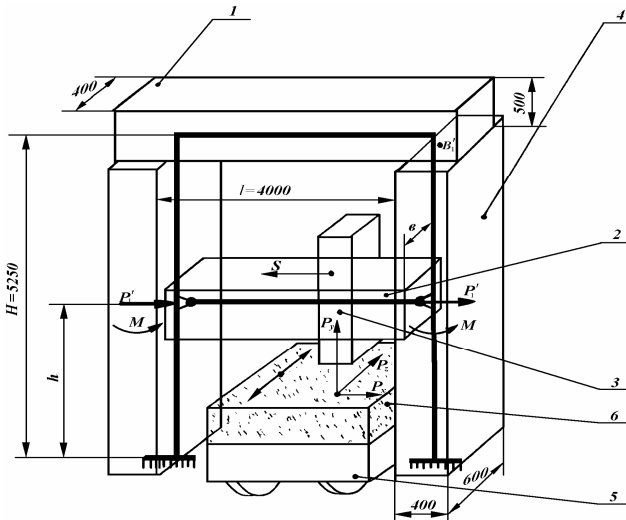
Розрахункова схема порталу: 1 – балка; 2 – траверза; 3 – каретка; 4 – колона; 5 – робочий стіл; 6 – кам'яний блок;
